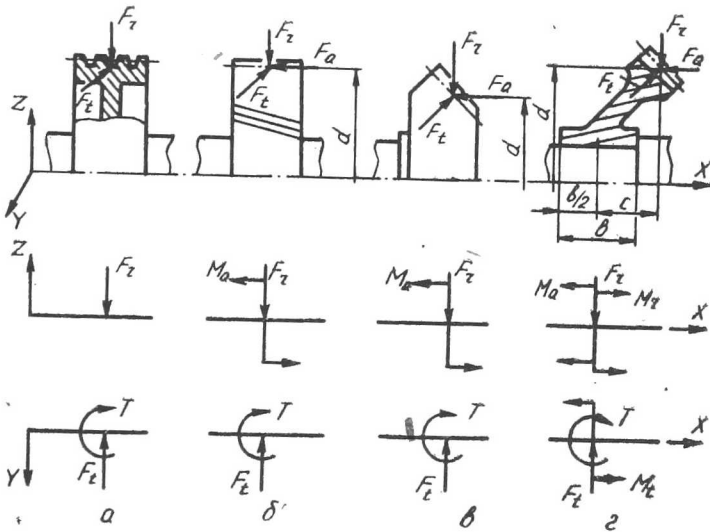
К определению точек приложения нагрузок на расчетной схеме
